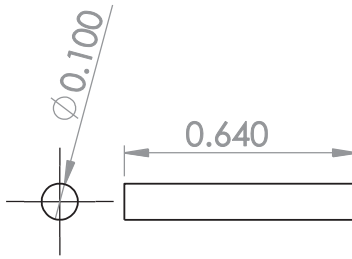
Dimensiones de la varilla pequeña de la parte superior de la montura lineal.
